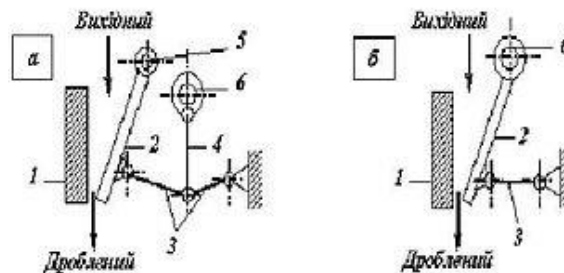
Схеми щоківих дробарок: а - з простим рухом щоки, б - зі складним рухом щоки: 1 - нерухома щока; 2 - рухома щока; 3 - розпірні плити; 4 - шатун; 5 - вісь; 6 - ексцентриковий вал.
